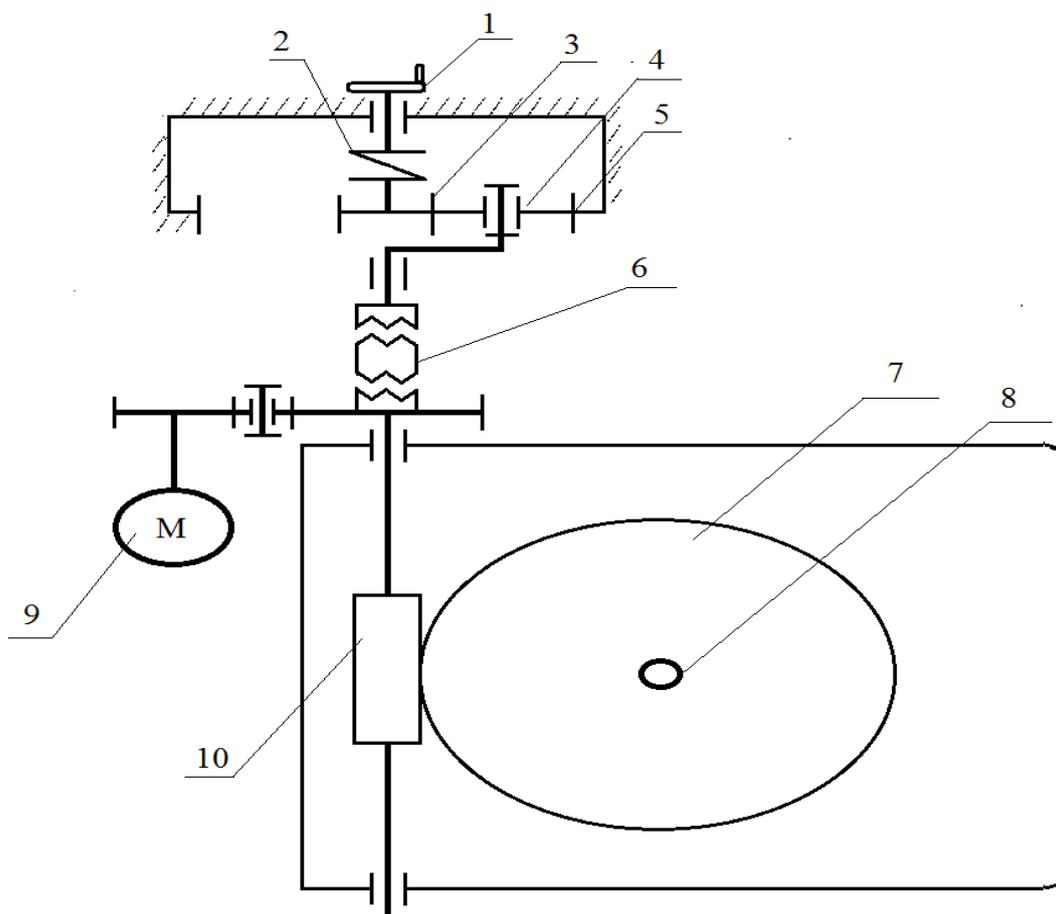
Кинематическая схема электропривода с ручным дублером на основе планетарной передачи
